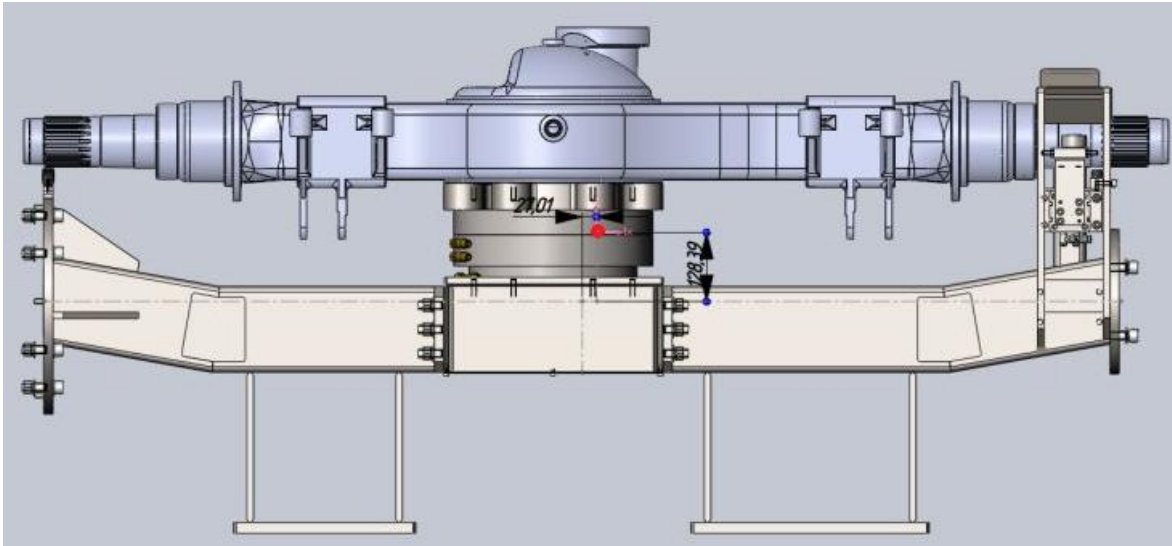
Primeiro protótipo do *Jig* de soldadura
